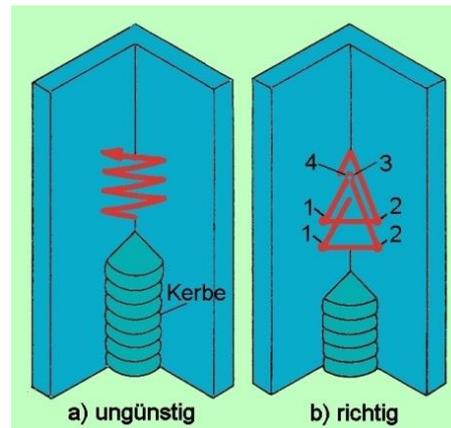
Empfehlungen zur Elektrodenführung für das Steignachtschweißen; Bildquelle: Der Schweißer / Informationen für Praktiker, DVS-Verlag, 9/2009
